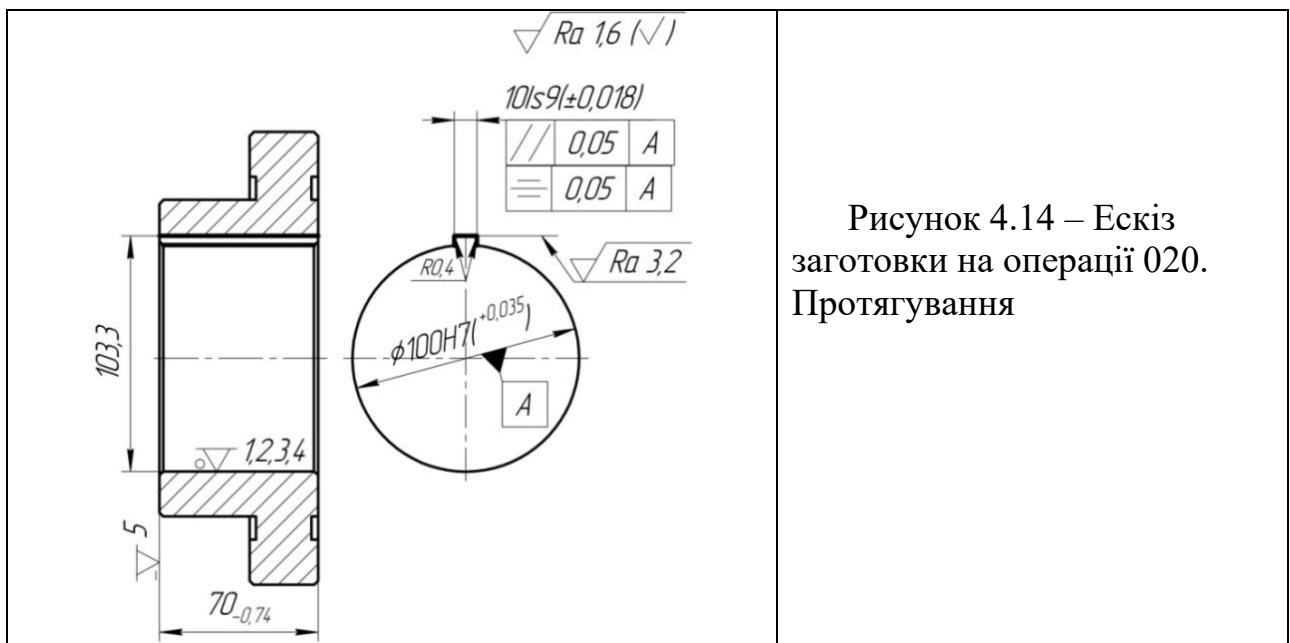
Ескіз заготовки на операції 020. Протягування
